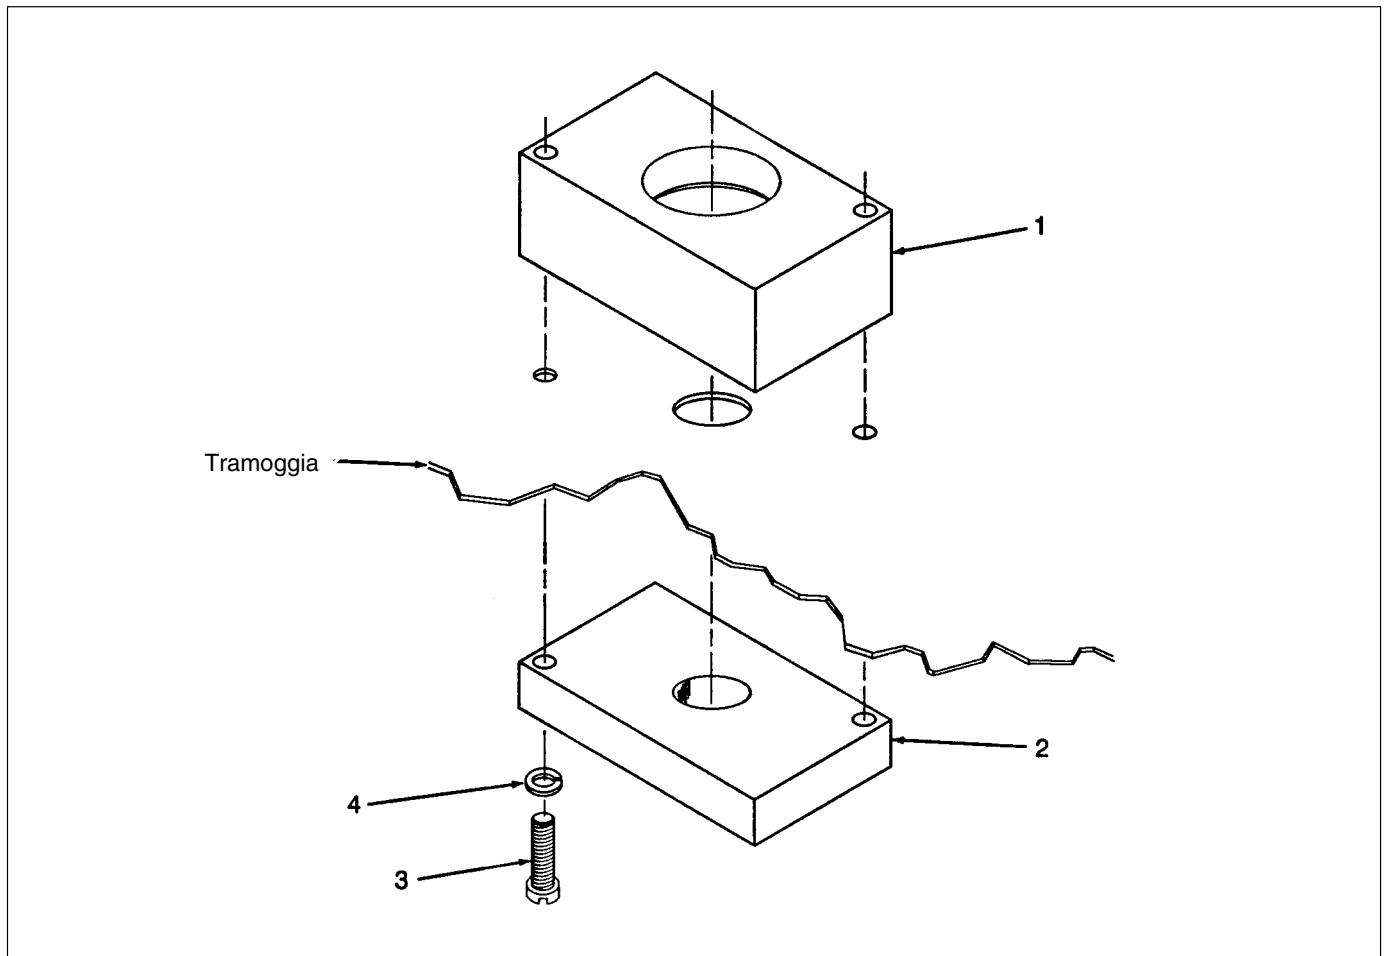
Composição do kit de montagem de uma bomba simples
